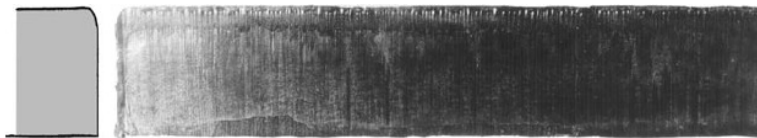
Boquilla de oxicorte demasiado cerca.
